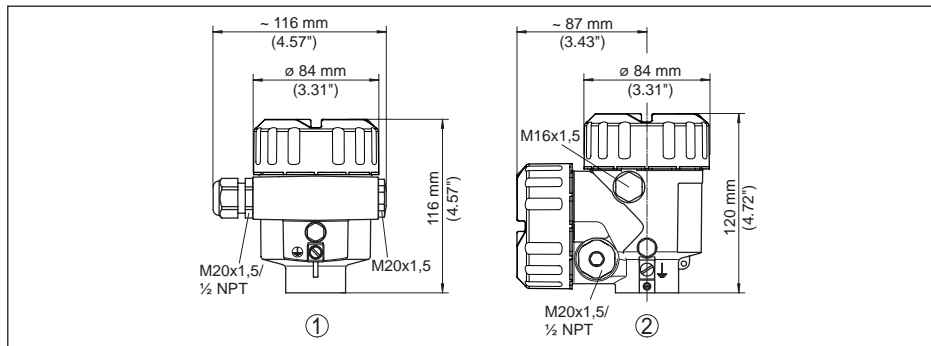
Корпуса в исполнении IP 66/IP 68 (0,2 bar), (с установленным модулем индикации и настройки корпус выше на 9 мм/0.35 in)
